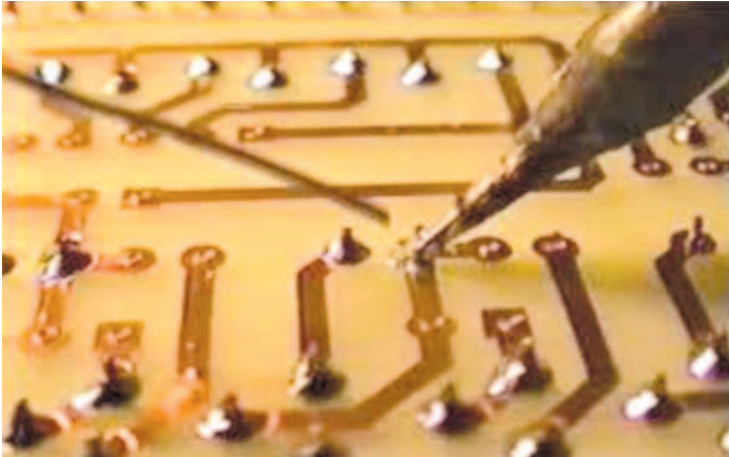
Soldadura blanda. Empalme electrónico
